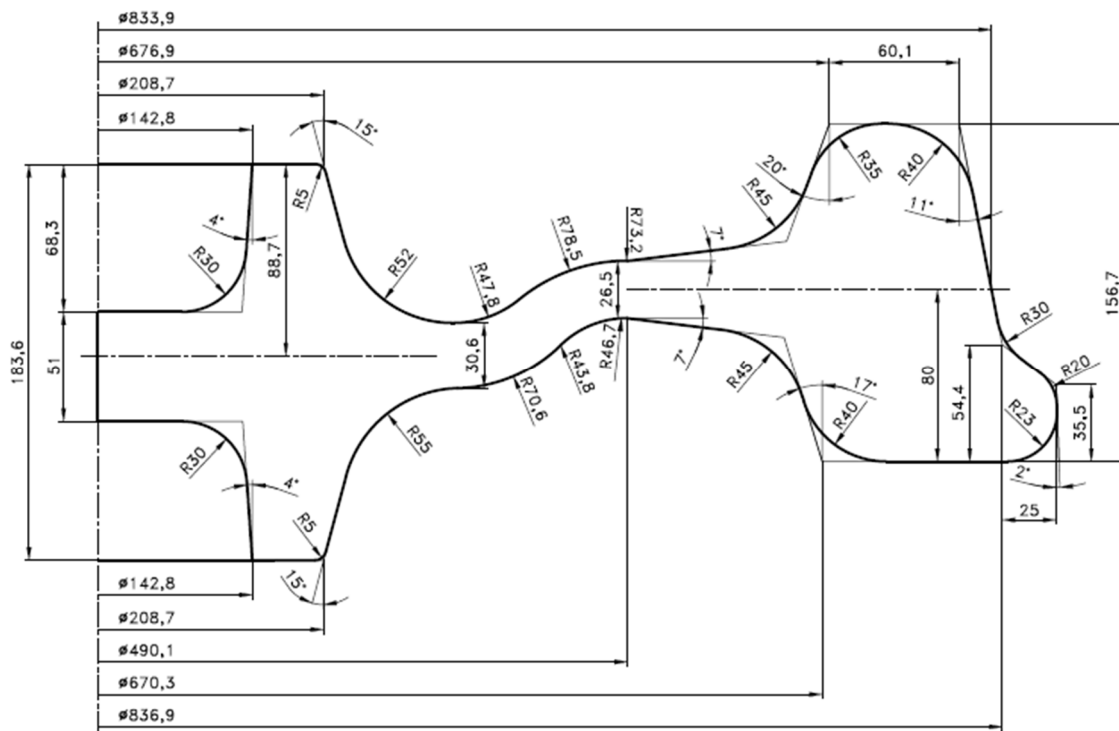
Чертеж колесной заготовки, полученной в формовочном штампе (калибровка для формовочного прессы)
